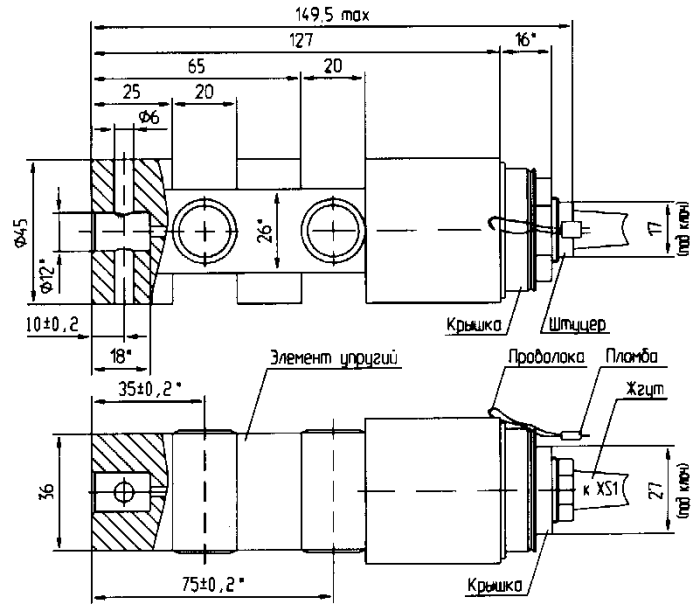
Габаритные и присоединительные размеры ДУс, ДУс-01
